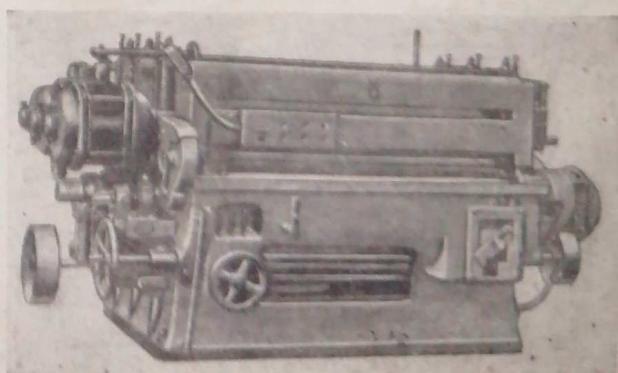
Двусторонний 6-цилиндровый шлифовальный станок
